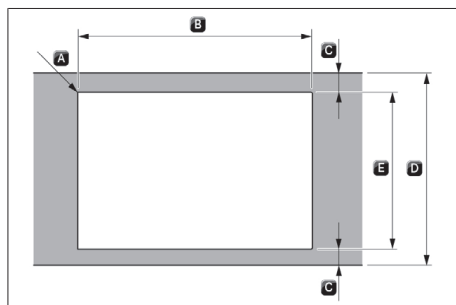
Dimensiones de recorte para montaje superpuesto
